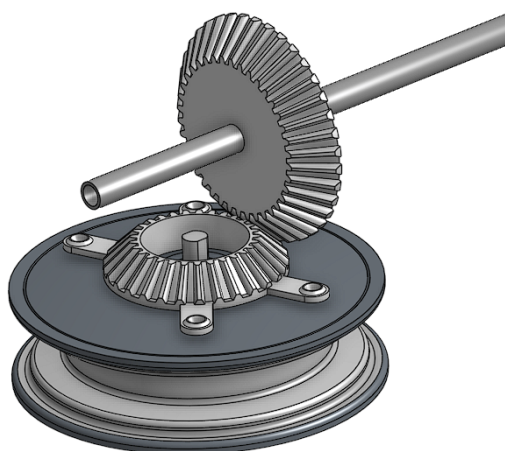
Vista isométrica del ensamblaje de la transmisión con engranajes cónicos con el motor en Onshape [fuente: elaboración propia]
